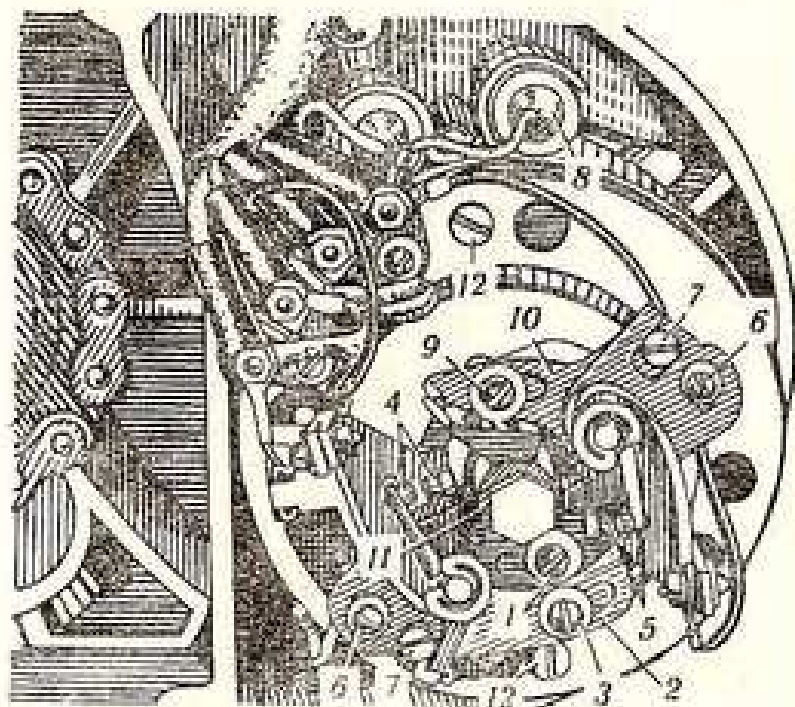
ГЕНЕРАТОР С ПРЕРЫВАТЕЛЯМИ:
